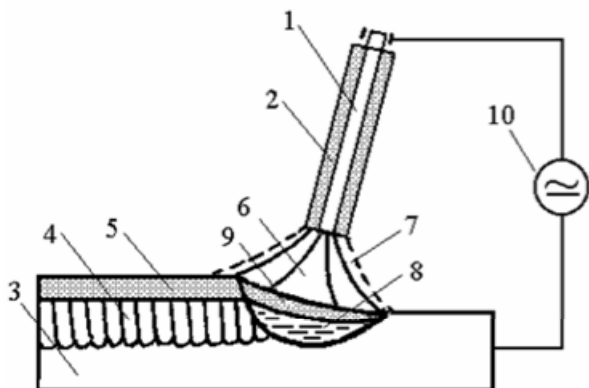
Схема ручной дуговой сварки плавящимся электродом с покрытием: 1 – стержень электрода, 6 – электрическая дуга, 2 – покрытие электрода, 7 – газовая защитная атмосфера, 3 – основной металл 8 – жидкая металлическая ванна, 4 – сварной шов, 9 – жидкая шлаковая ванна, 5 – твердая шлаковая корка 10 – источник тока
